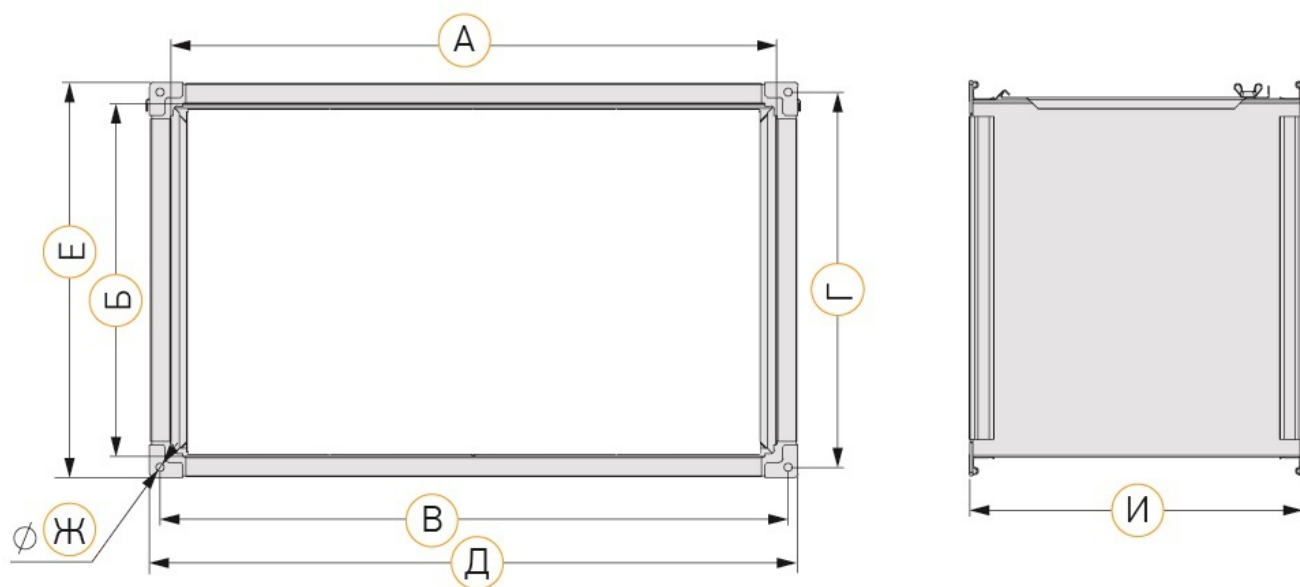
Внешний вид и основные размеры фильтров KPR
